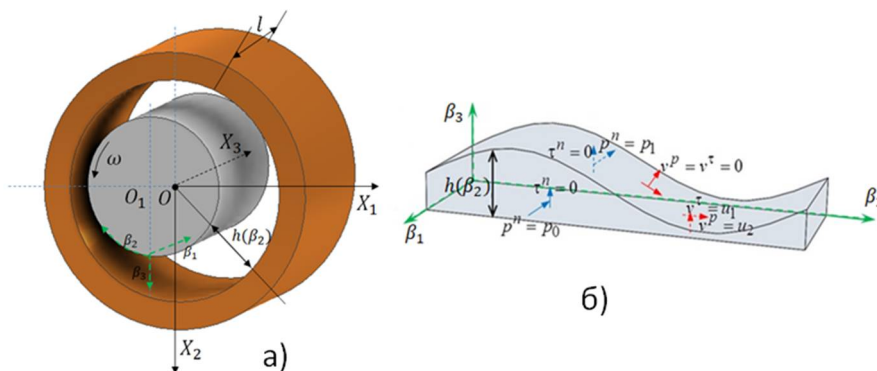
Схема подшипника и развертка смазочного слоя в цилиндрических координатах
